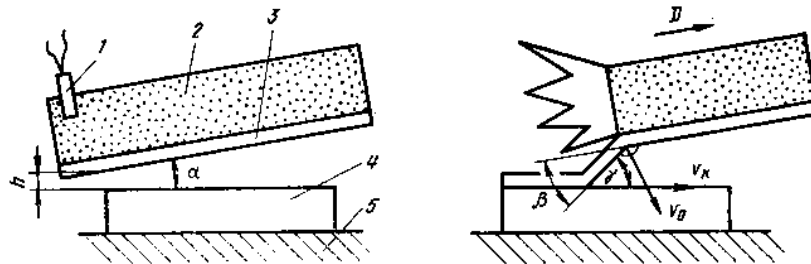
Схема сварки взрывом под углом:
